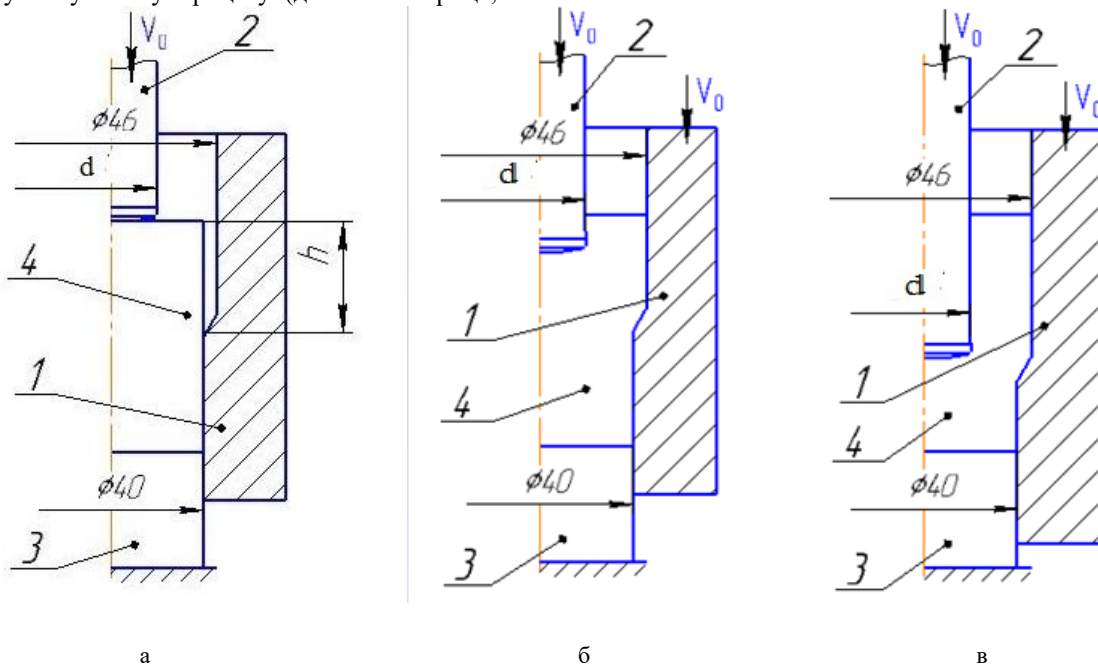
Розрахункова схема зворотного видавлювання з роздачою
